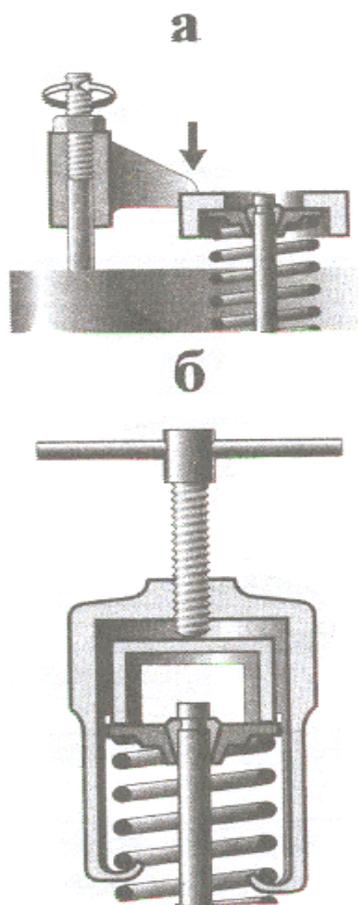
Рычажное приспособление для разборки/сборки пружин клапанов, применяемое без снятия головки с блока цилиндров
